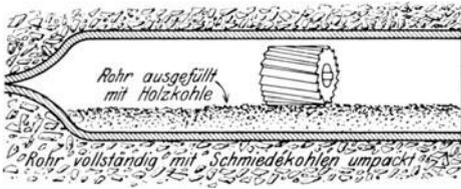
Altes Stück Gasrohr zur Muffel zurechtgemacht.
